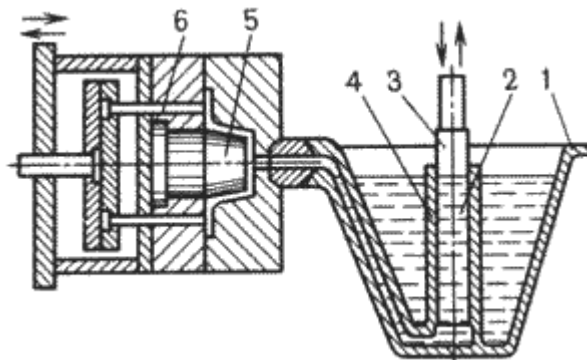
Схема изготовления отливки на машинах с горячей камерой прессования
